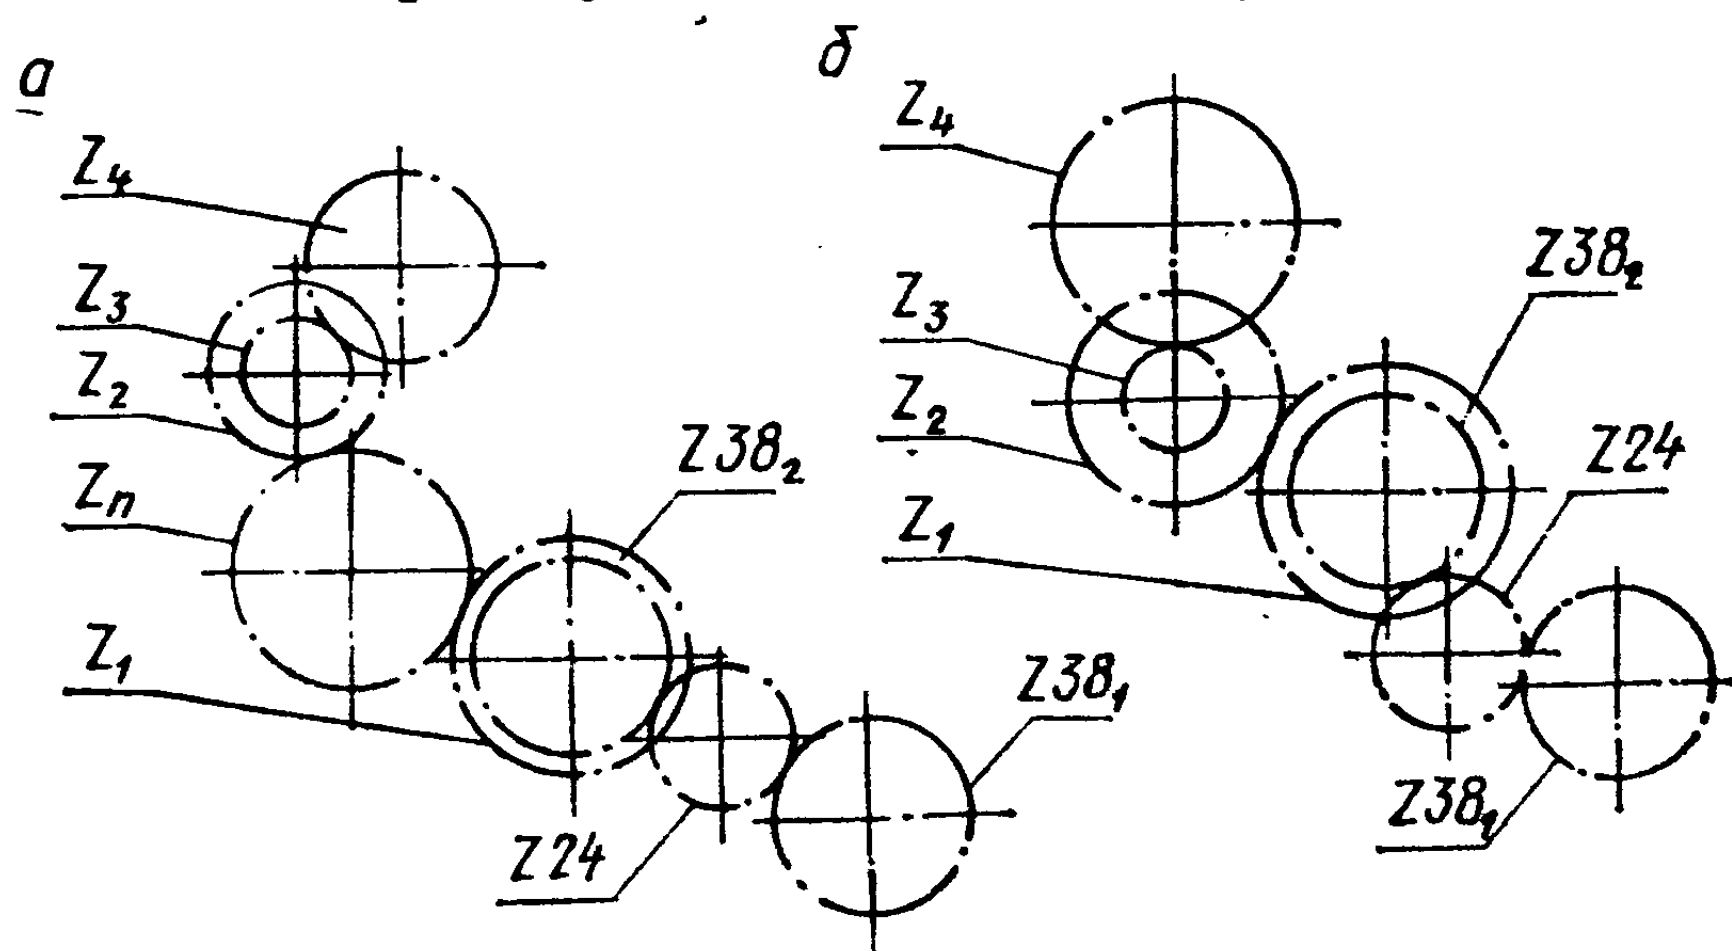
Схемы настройки гитары сменных зубчатых колес для фрезерования винтовых канавок.
